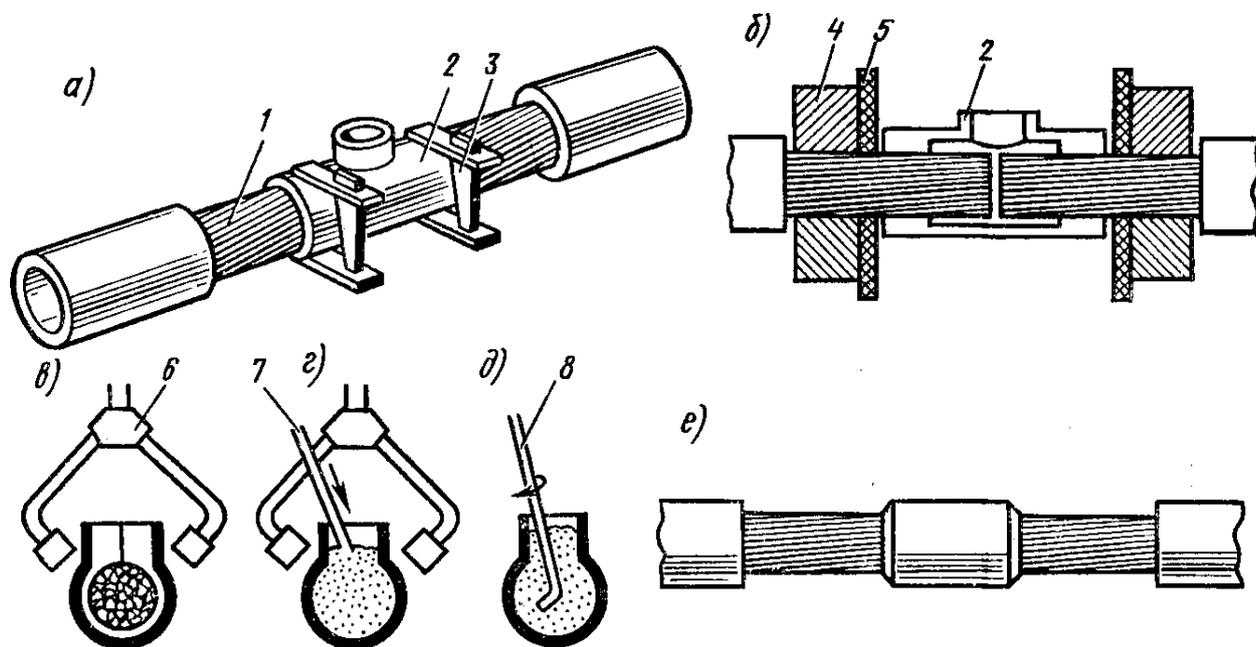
Последовательность операций при пропано-кислородной сварке стыковых соединений жил: *а, б* - подготовка к сварке; *в* - нагрев; *г* - введение присадки с подогревом; *д* - перемешивание сварочной ванны; *е* -- готовое соединение; 1 - жила; 2 - сварочная форма; 3 - клин; 4 - охладитель; 5 - экран из листового асбеста; 6 - газовая горелка; 7 - присадочный пруток; 8 - мешалка
